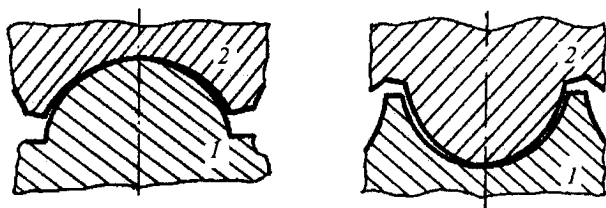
Коловий профіль витків черв'яка і зубів черв'ячного колеса
